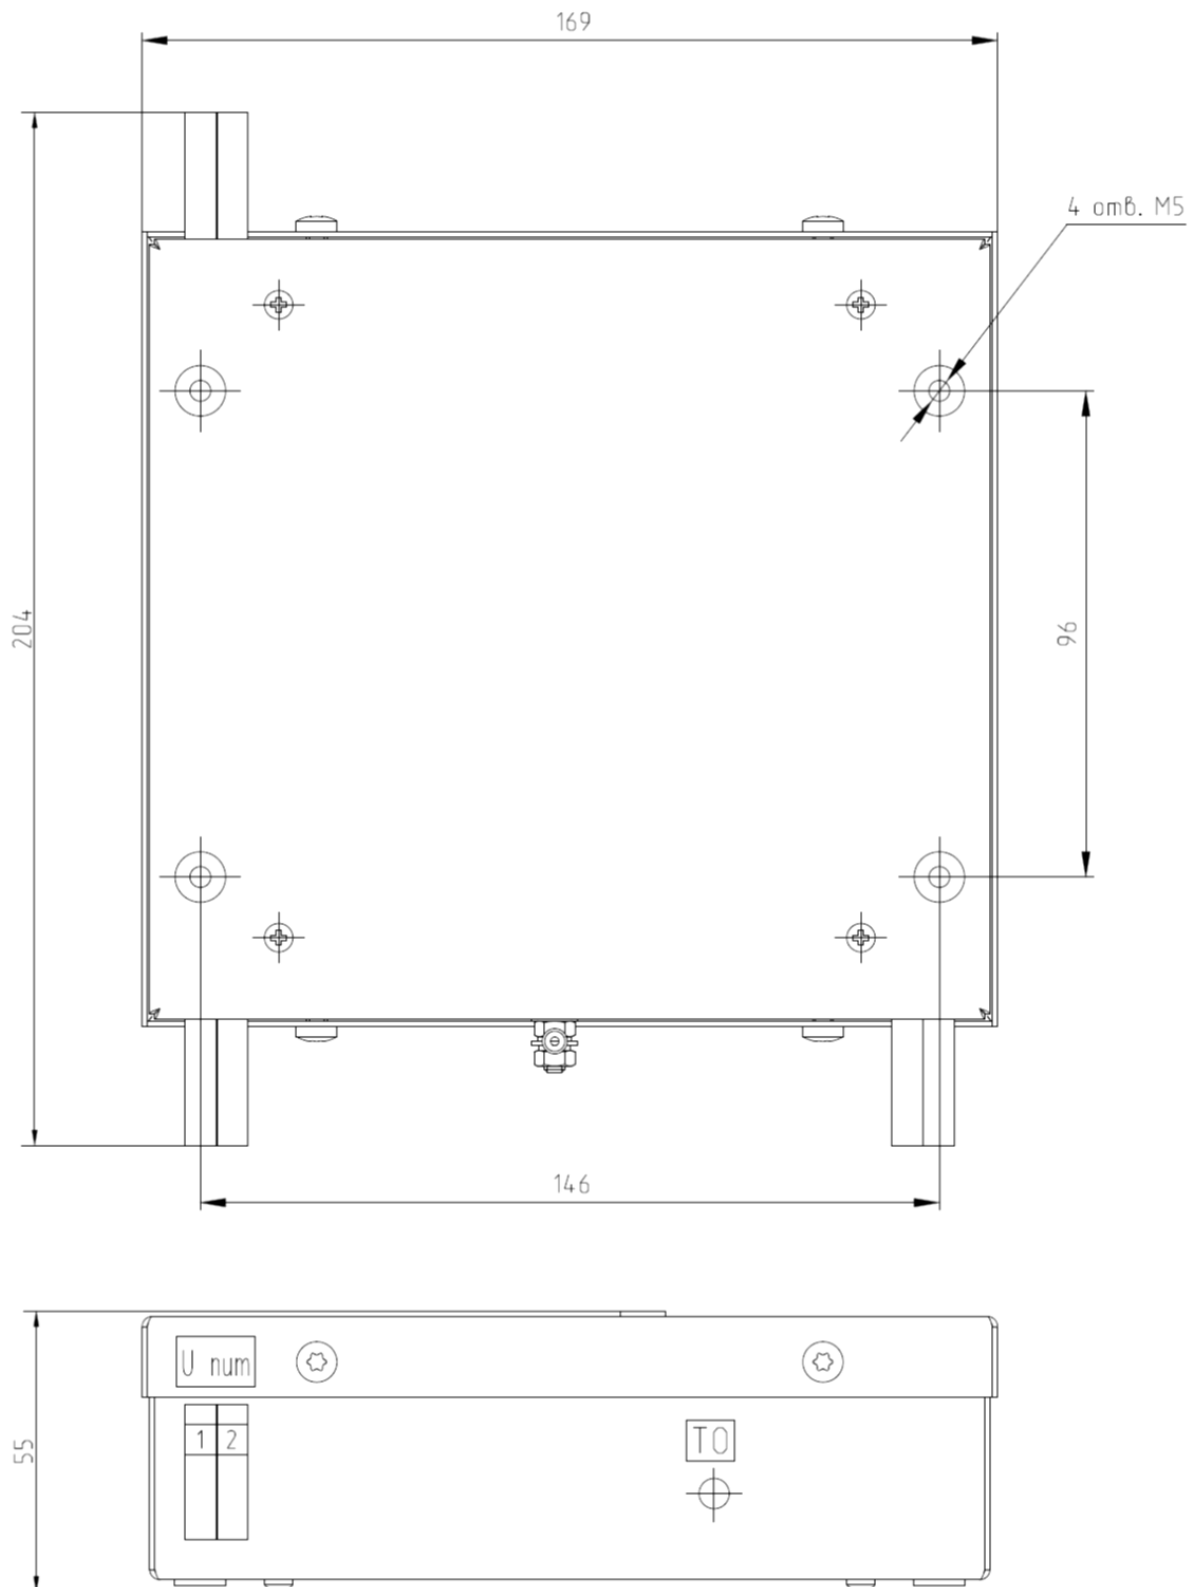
Габаритные и установочные размеры блока БР-1000
